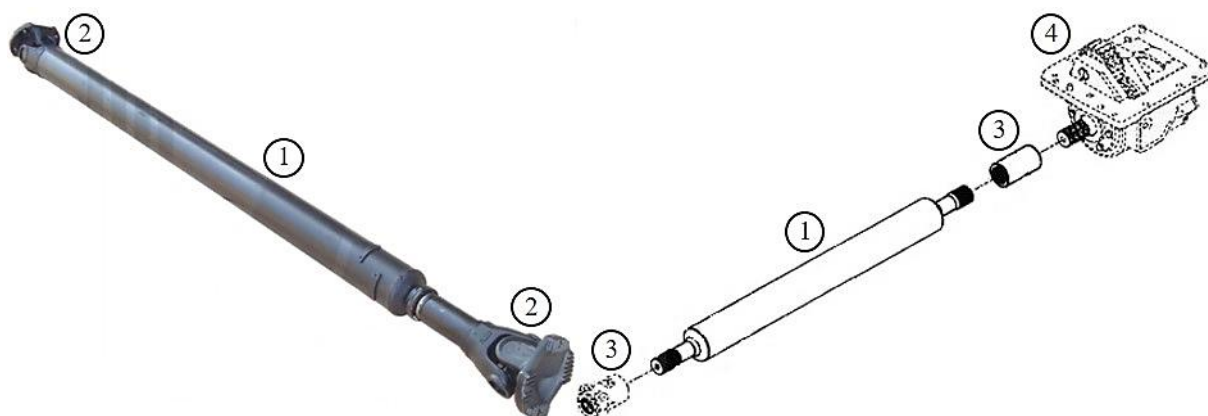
Primárně spojená spojka pohonu přední nápravy traktoru [3]
